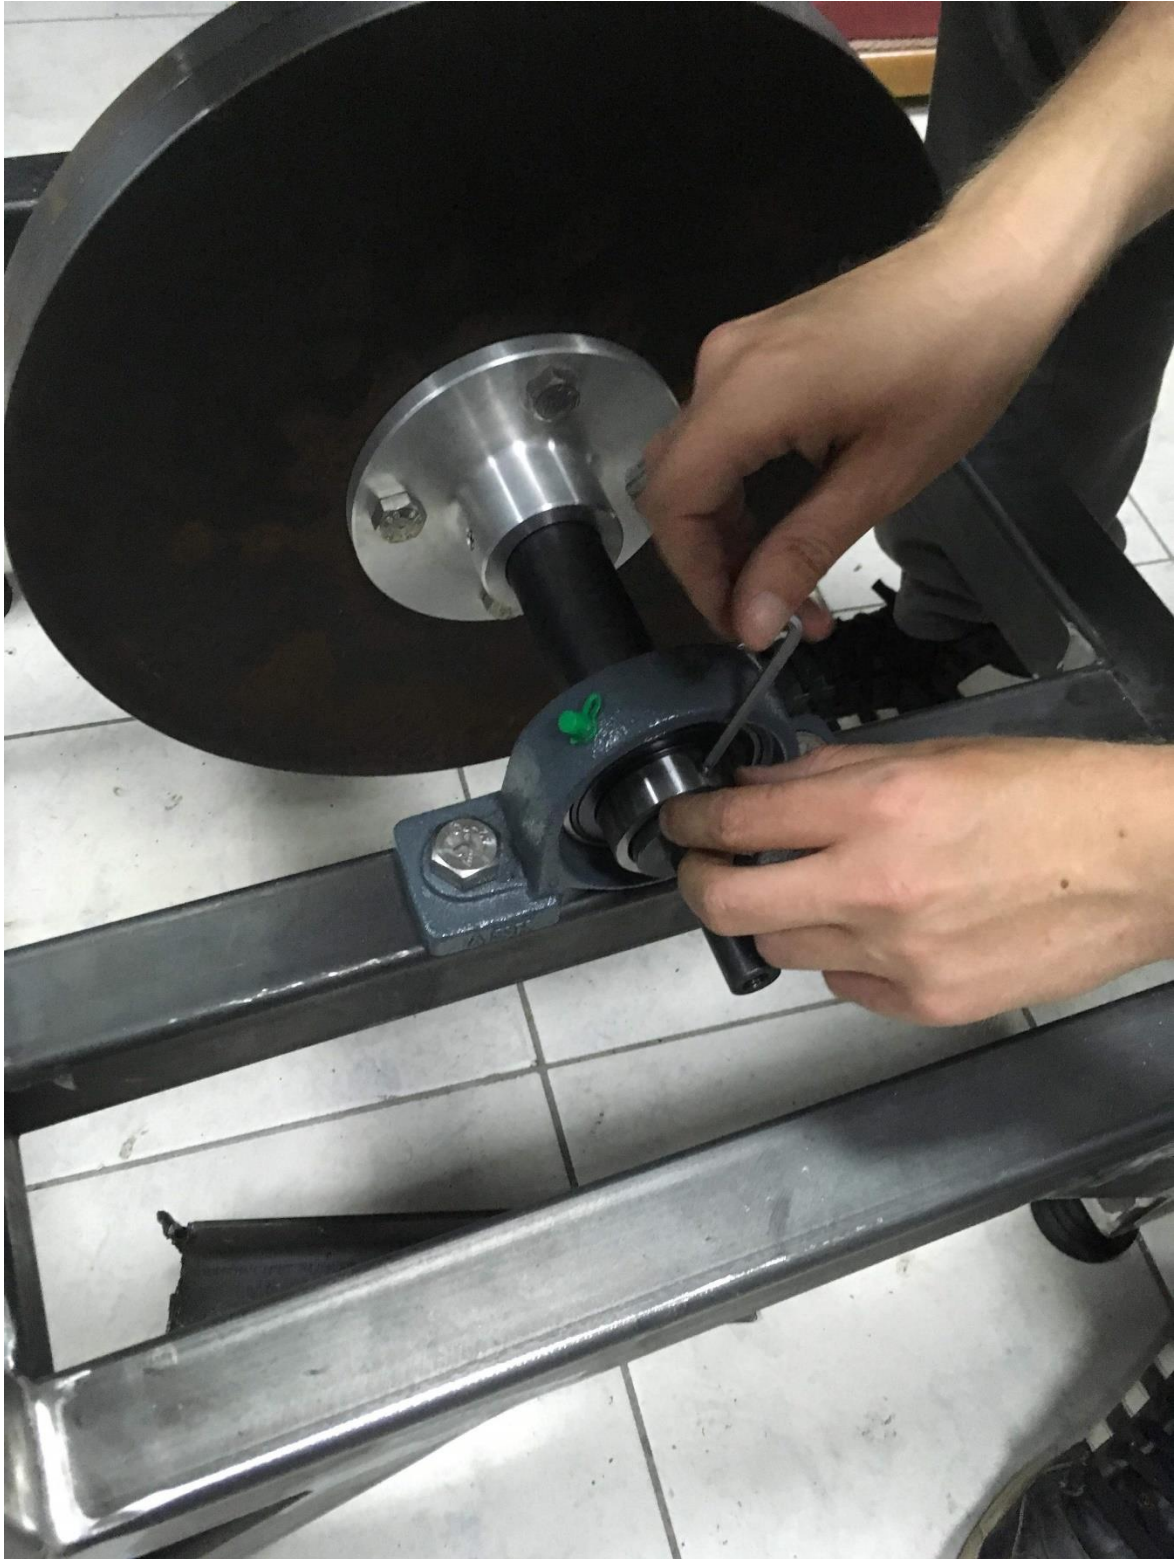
Εμπρόσθιο ράουλο POS20_CD_FRONT DRUM_SUB ASSEMBLY.
